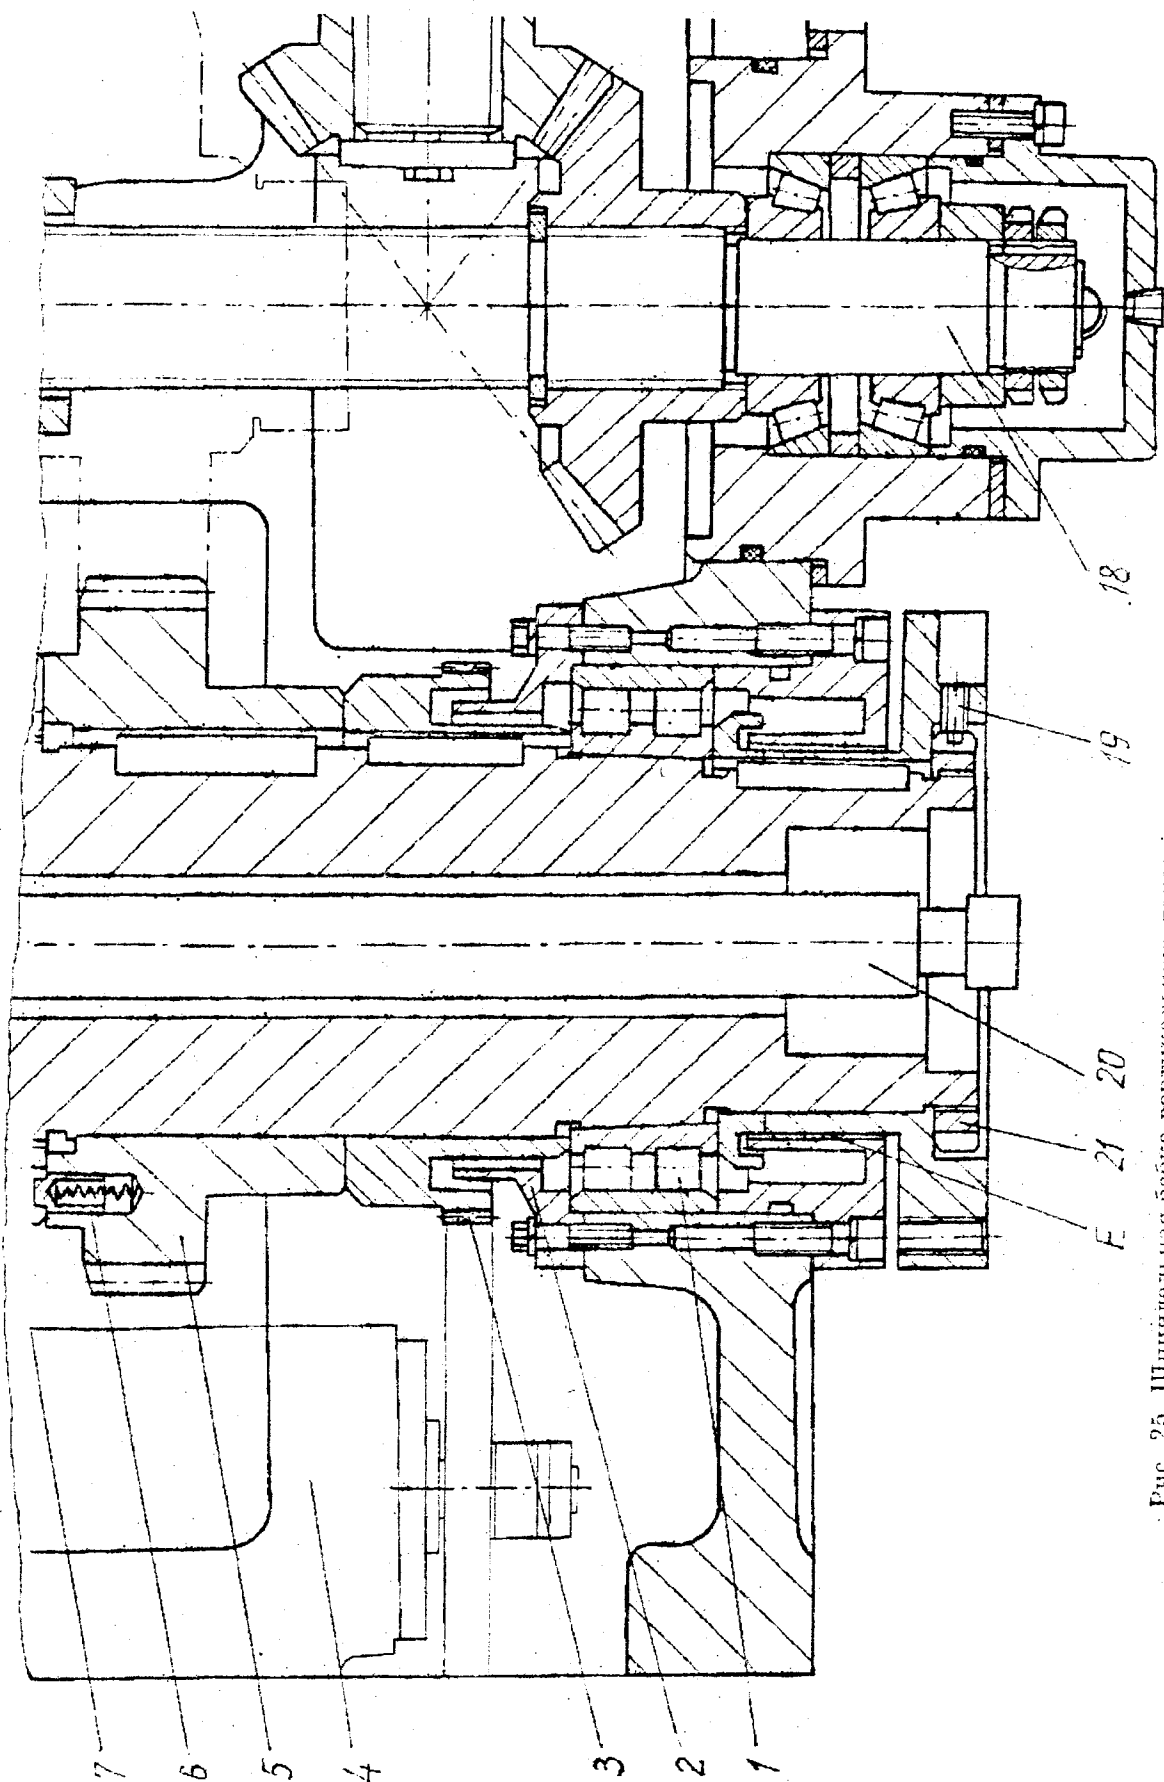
Шпиндельная бабка вертикального токарного станка с ЧПУ.
